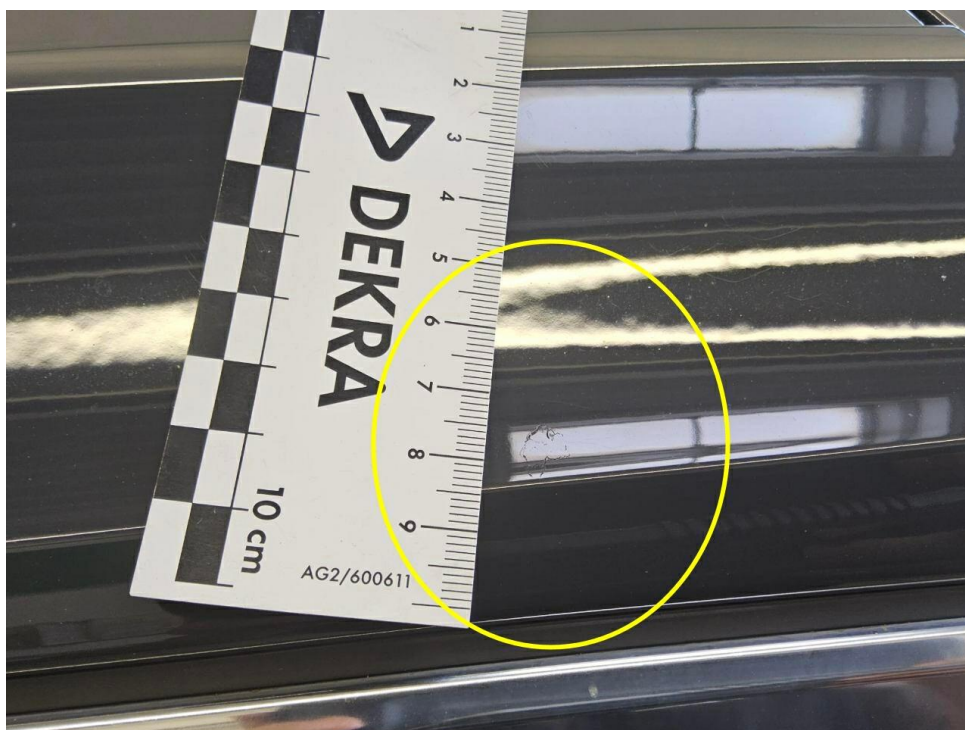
Dachrahmen links Lackierung, Umweltschaden, lackieren mit Lackaufbau
